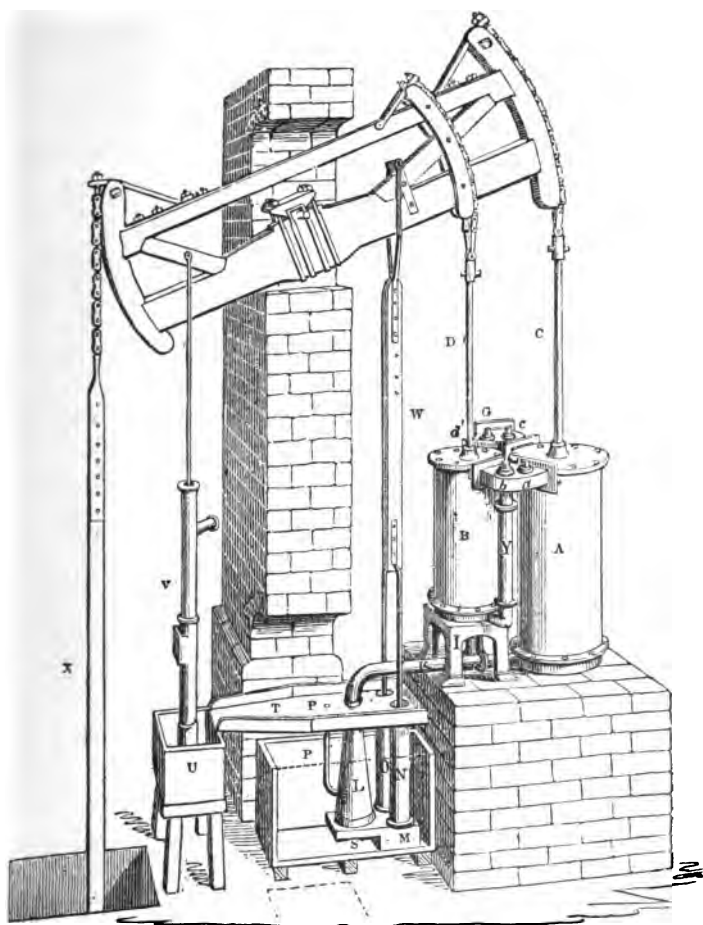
Machine à deux cylindres successifs de Hornblower :
